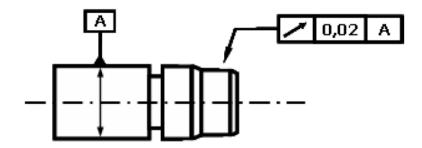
Indicação de tolerância de batida radial em desenho técnico
